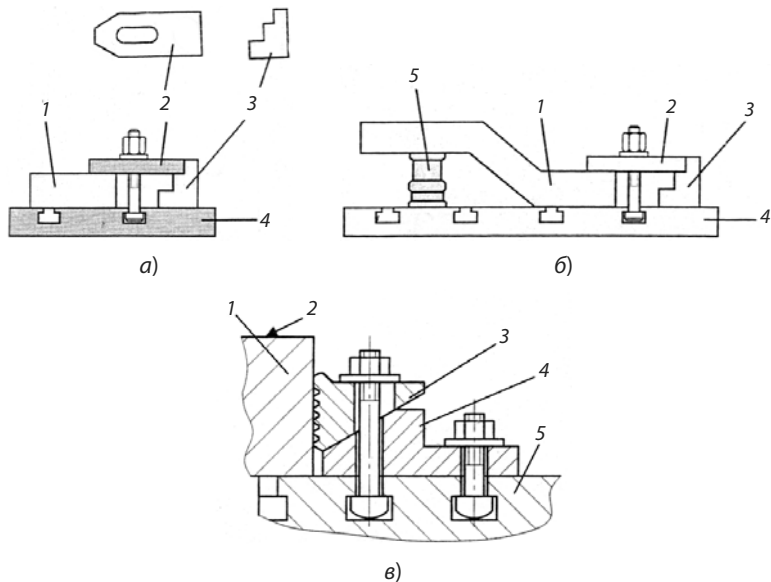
Схема установки и закрепления заготовок прихватами:
